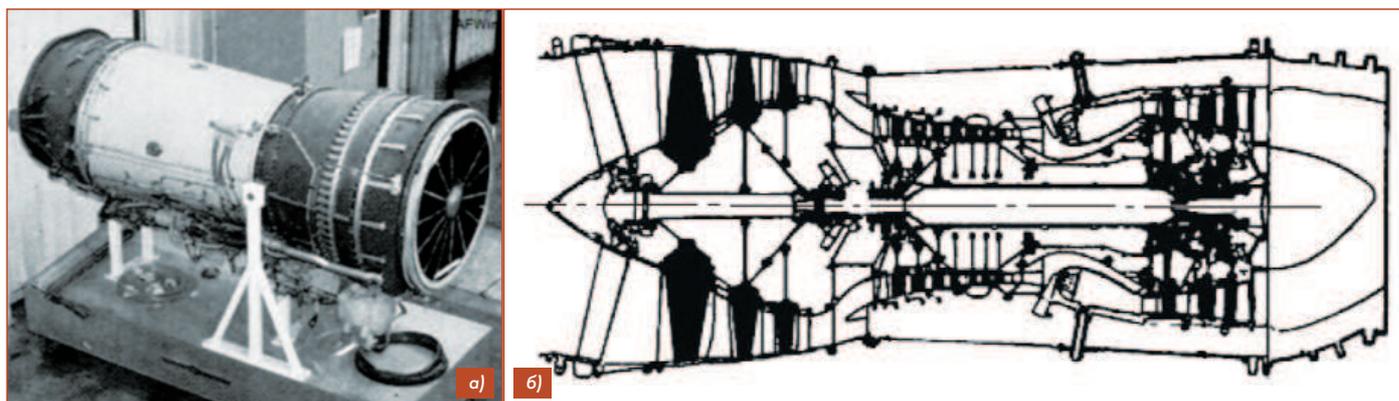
РДД F412: а) внешний вид; б) конструктивная схема
